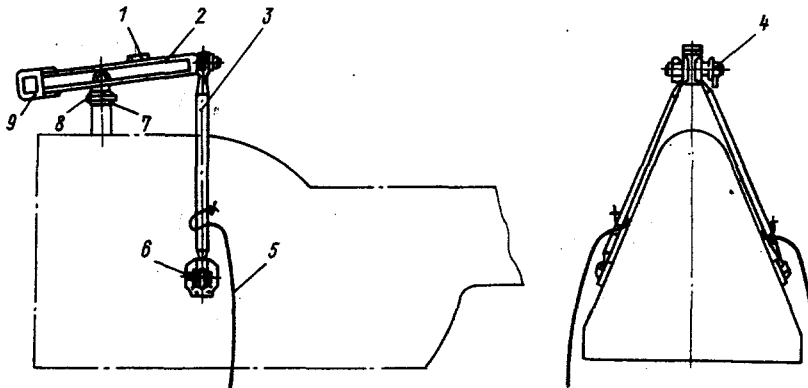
Приспособление для подъема вертолета без хвостовой балки (8AT-9945-00):
